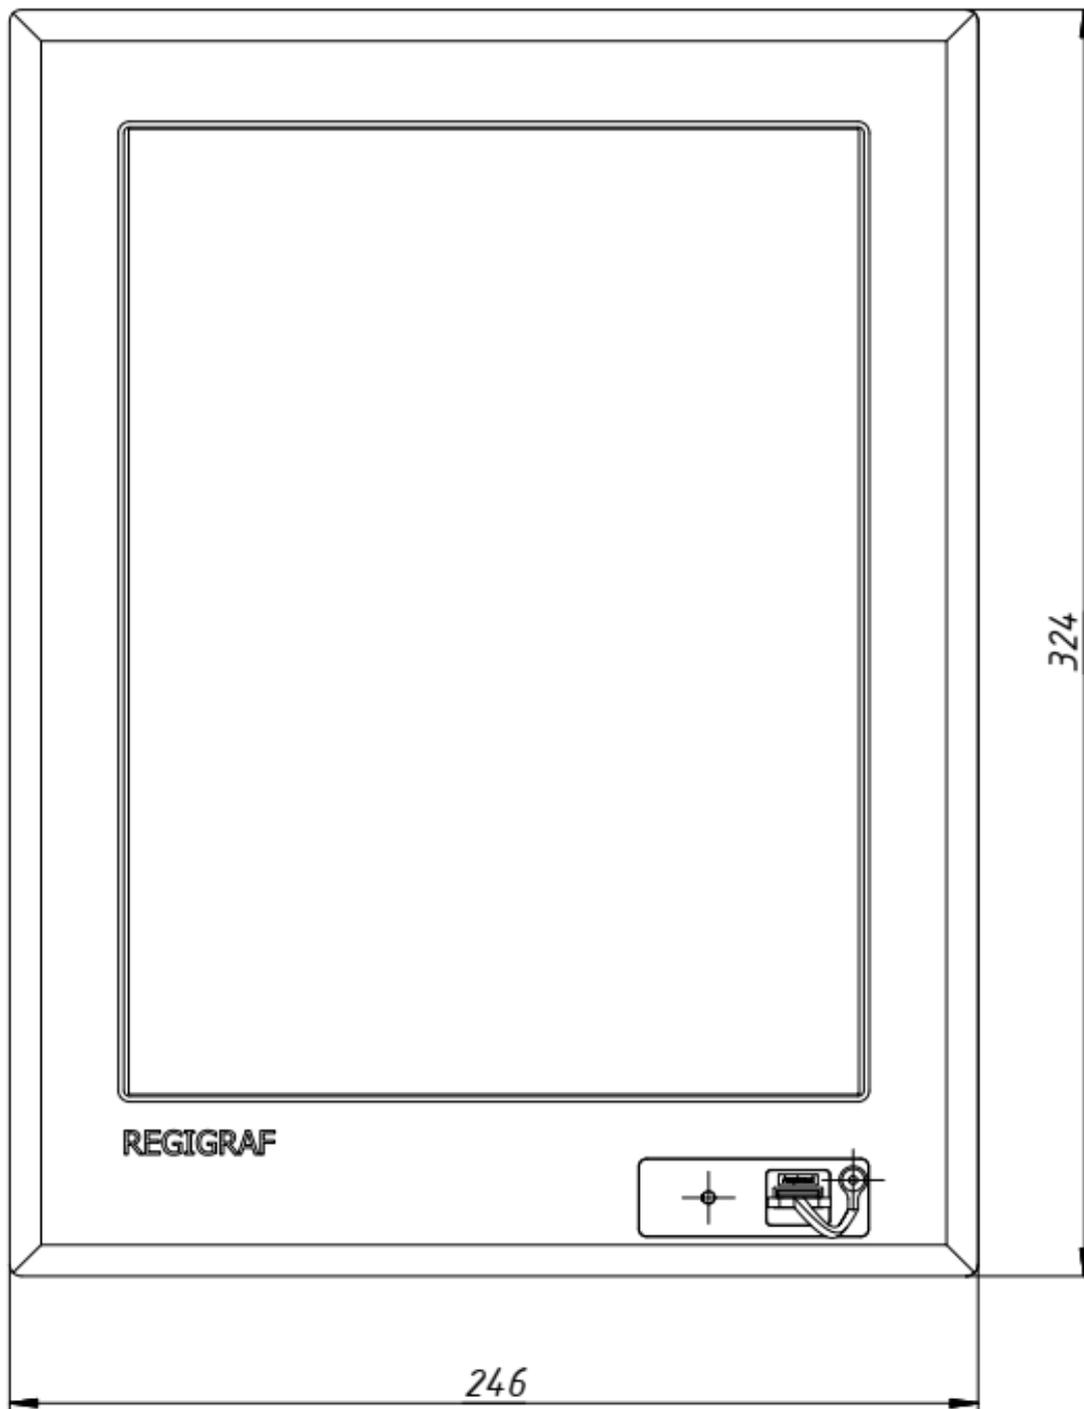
Габаритный чертёж прибора в исполнении Ф1772–2, вид спереди
